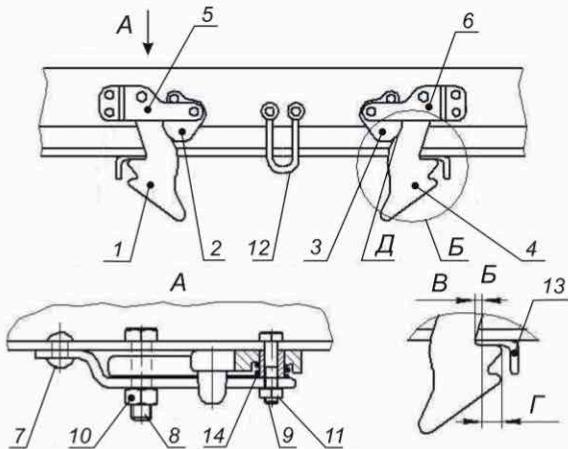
Запорное устройство крышки люка полуувагона модели 12-132-03:
